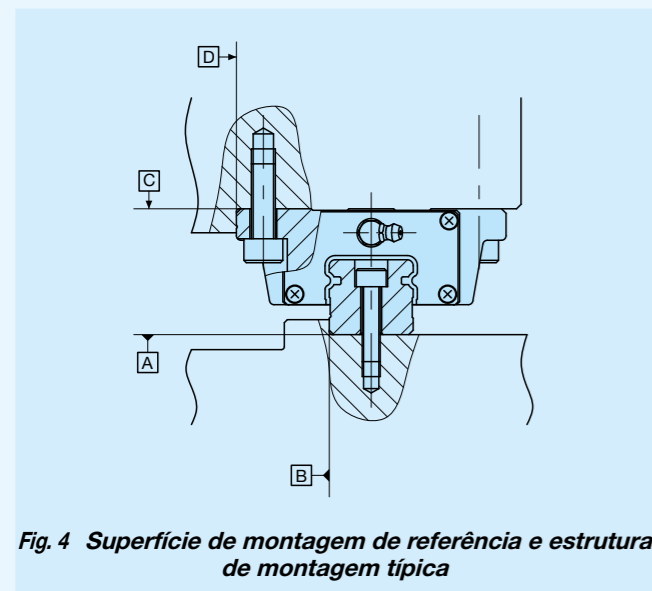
Superfície de montagem de referência e estrutura de montagem típica
